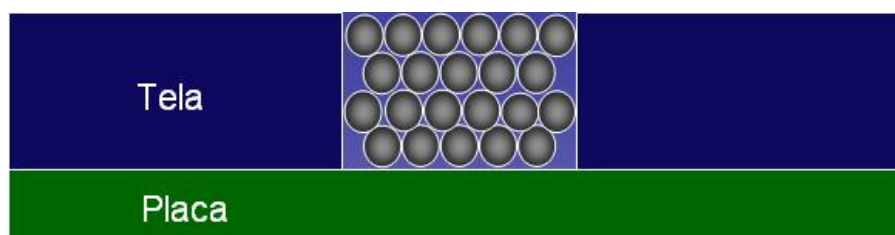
Regra básica para o número mínimo de bolas de solda a depositar num PCB
